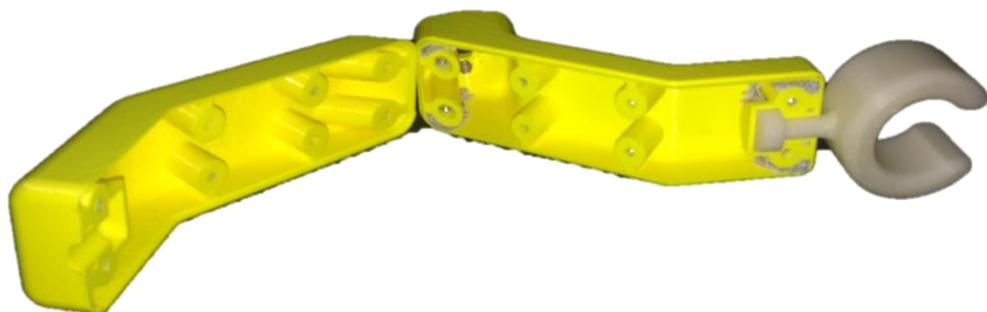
CONFIGURACIÓN DE PIEZAS PARA ENSAMBLE
